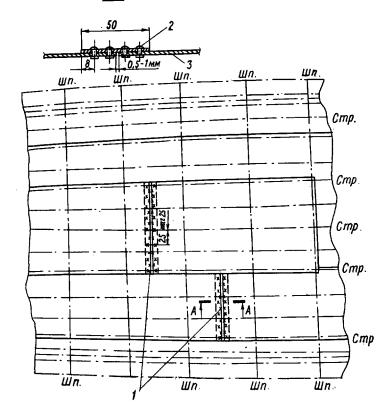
Стыковка листов обшивки при частичной замене: 1 — накладки Д16АТ-л.1,0; 2 — заклепки 3560А-3-6; 3 — листы обшивки Д16АТ-л.0,8
